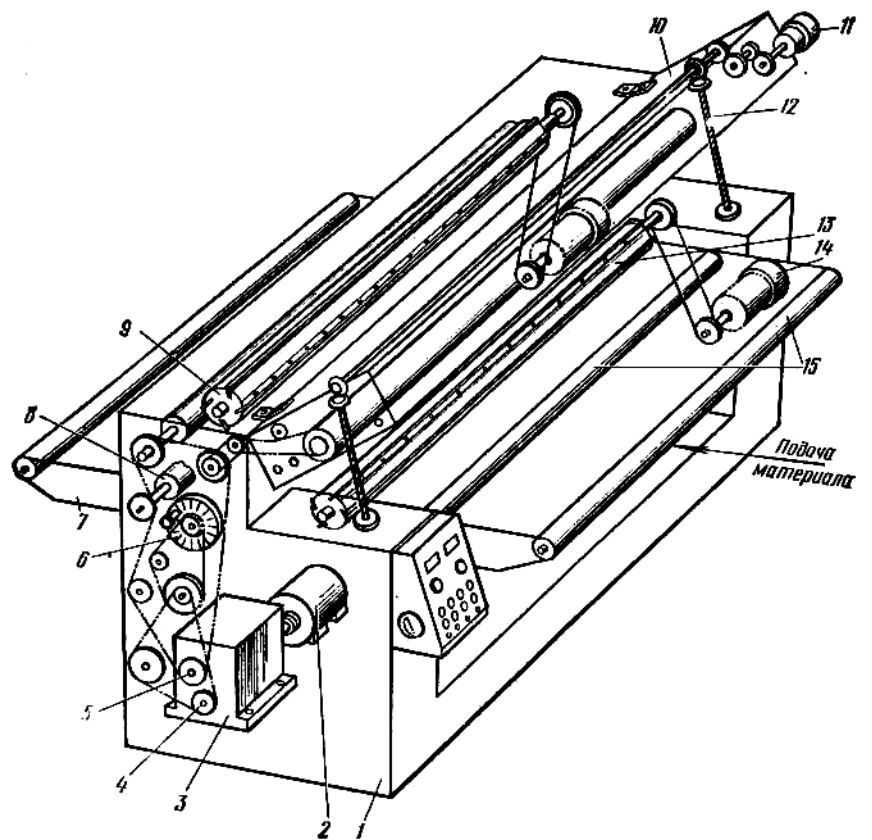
Двусторонний рейсмусовый станок С2Р12-2:
